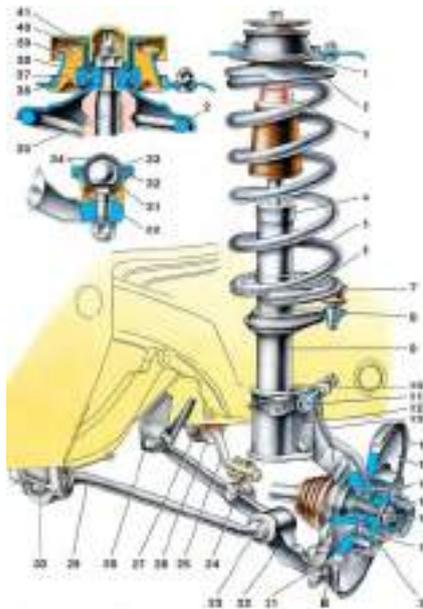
Передняя подвеска типа Мак-Ферсон в сборе: 1 – верхняя опора телескопической стойки; 2 – верхняя опорная чашка; 3 – буфер хода сжатия с защитным кожухом; 4 – опора буфера сжатия; 5 – пружина подвески; 6 – нижняя опорная чашка пружины; 7 – шаровой шарнир рулевой тяги; 8 – поворотный кулак; 9 – телескопическая стойка; 10 – эксцентриковая шайба; 11 – регулировочный болт; 12 – кронштейн стойки; 13 – поворотный кулак; 14 – защитный кожух переднего тормоза; 15 – диск тормозного механизма; 16 – стопорное кольцо; 17 – гайка ступицы колеса; 18 – шлицевой хвостовик корпуса шарнира привода колеса; 19 – направляющий штифт; 20 – подшипник ступицы колеса; 21 – шаровой шарнир; 22 – рычаг подвески; 23 – регулировочные шайбы; 24 – стойка стабилизатора; 25 – штанга стабилизатора; 26 – подушка штанги стабилизатора; 27 – кронштейн крепления штанги стабилизатора; 28 – кронштейн кузова для крепления рычага подвески; 29 – растяжка рычага подвески; 30 – кронштейн крепления растяжки; 31
